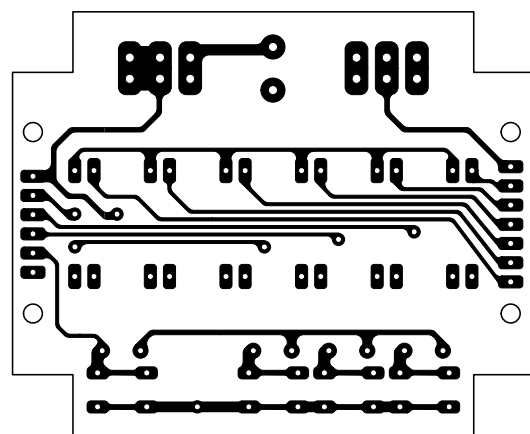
Dessin, à l'échelle 1, du circuit imprimé double face à trous métallisés de la platine des LED EN1676A, côté soudures.
